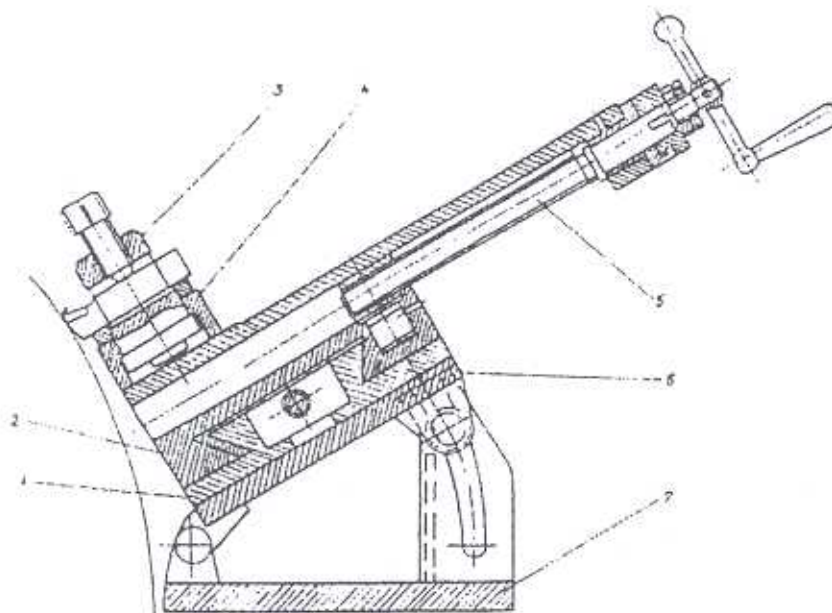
Приспособление для проточки контактных колец и вала ротора
